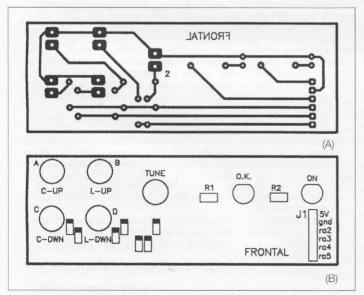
Plantilla de la placa para el panel frontal (A) y disposición de componentes (B).
